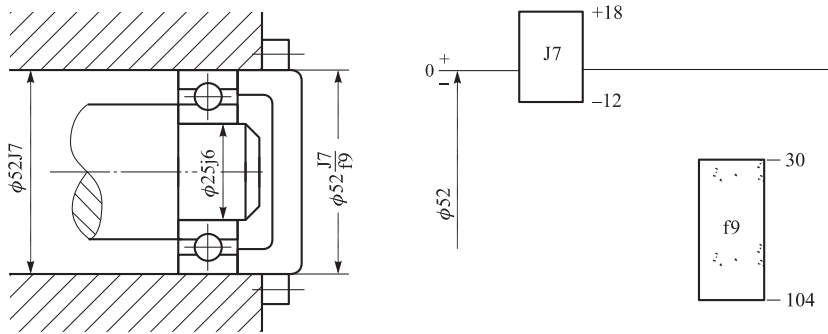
箱体孔与滚动轴承和轴承端盖的配合
